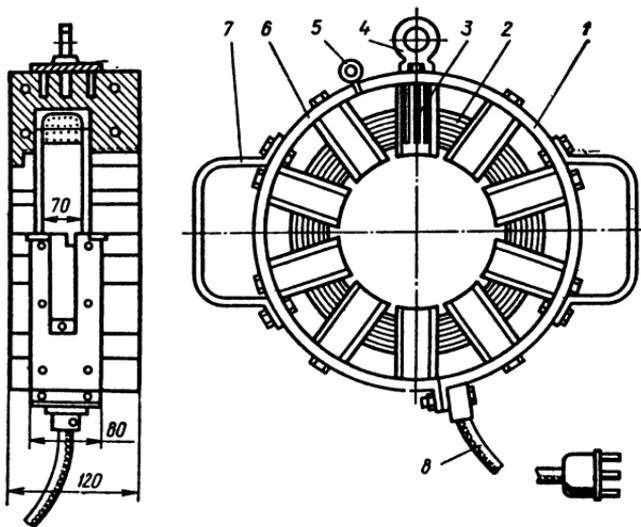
Схема приспособления для разогрева демонтируемой втулки:
